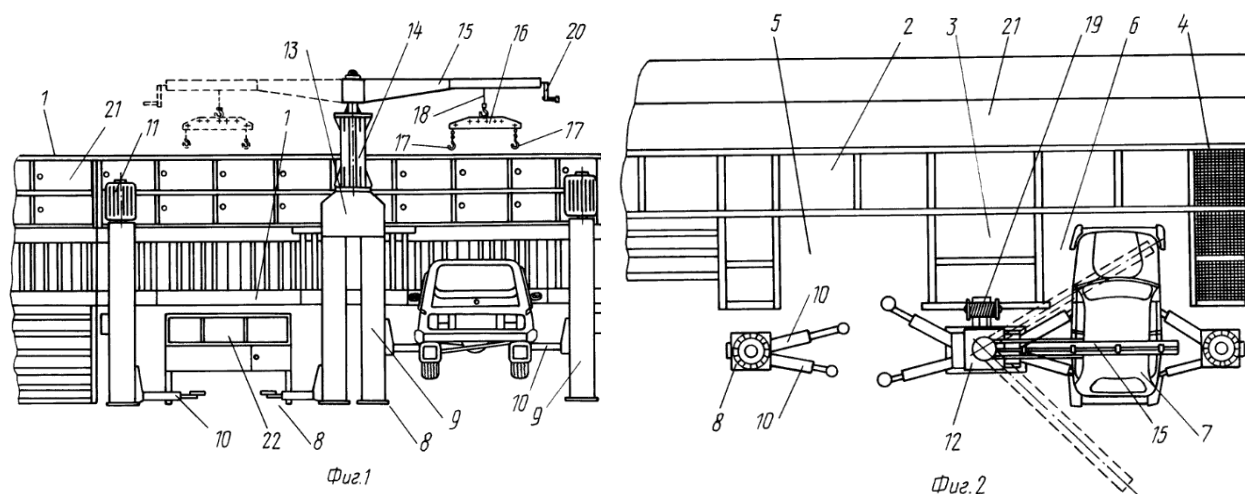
Сборочный стенд для монтажа автомобилей
